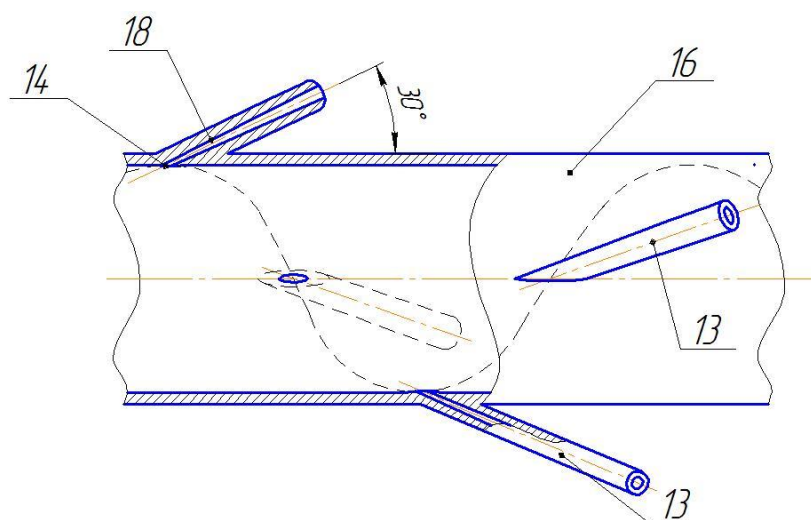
Устройство для промывки молокопроводов доильных установок
